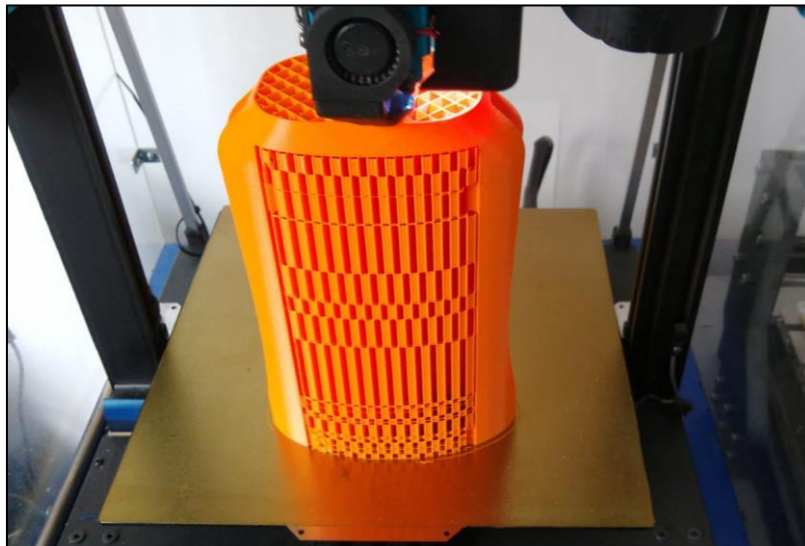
Impresión cuerpo del fuselaje con soportes [Autores].
